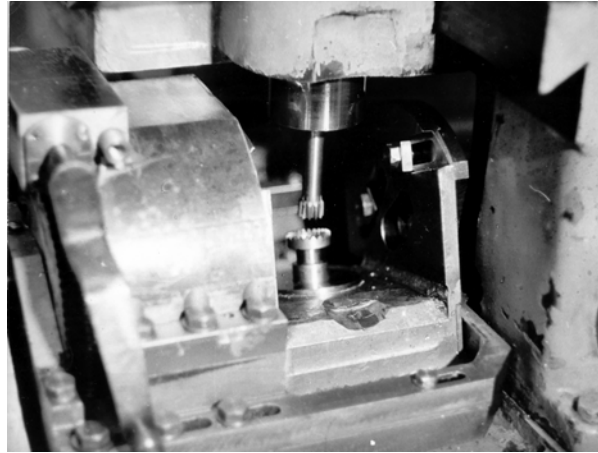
Tallado del engranaje biparamétrico con el uso de una talladora de engranes.
